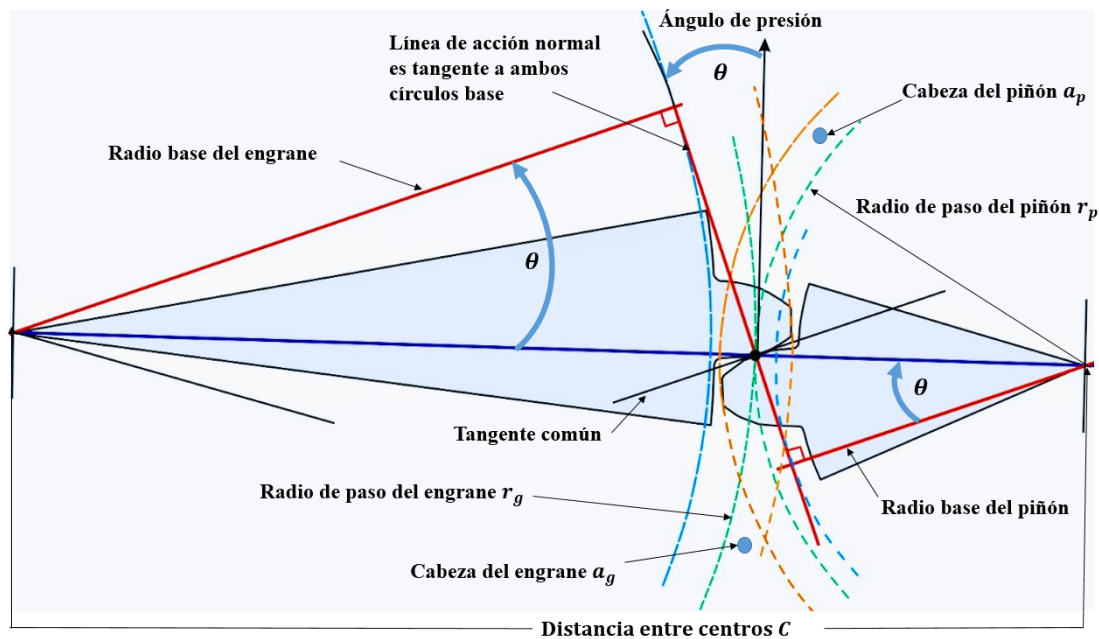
Geometría del contacto de engranes cilíndricos de dientes rectos.
